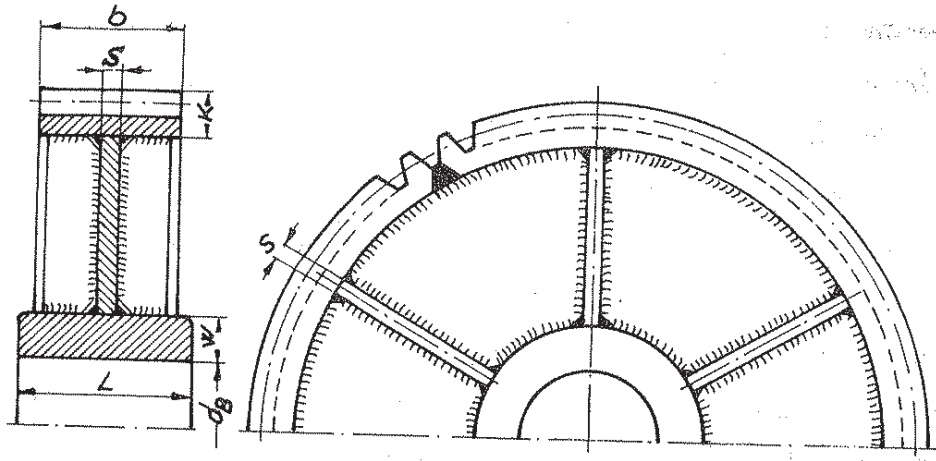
Kaynak konstrüksiyon büyük çarkların şekillendirilmesi [L. 12]
